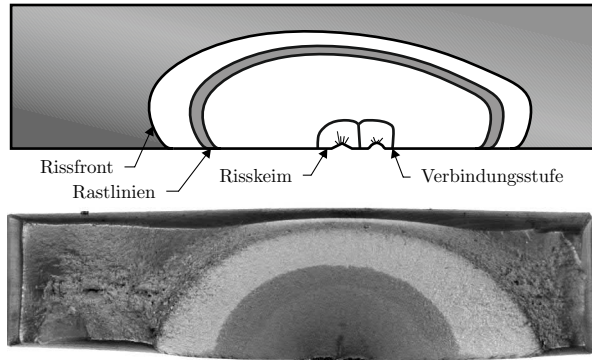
Darstellung einer typischen Ermüdungsbruchfläche als Schema (oben) und Bruchbildfoto (unten)
